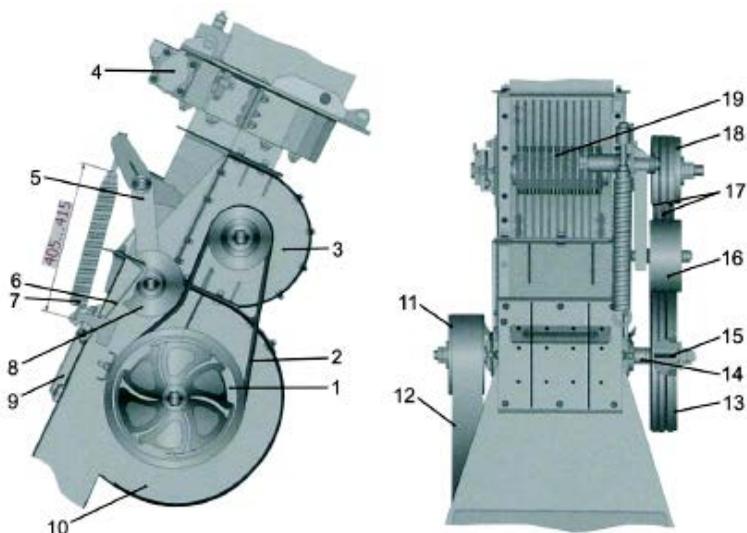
Установка доизмельчителя зерна: 1, 13 – шкив привода доизмельчителя зерна; 2 – ремень привода доизмельчителя; 3 – доизмельчитель зерна; 4 – устройство поворотное; 5 – рычаг натяжного устройства; 6 – направитель потока массы; 7 – пружина натяжного устройства; 8, 16 – шкив натяжной; 9 – крышка; 10 – конфузор с ускорителем; 11 – шкив привода ротора ускорителя массы; 12 – ремень привода ускорителя массы; 13 – ведущий шкив; 14 – вал ротора ускорителя массы; 15 – шпонка; 17 – ремни привода ротора доизмельчителя зерна; 18 – шкив привода ротора доизмельчителя зерна; 19 – ротор доизмельчителя зерна
